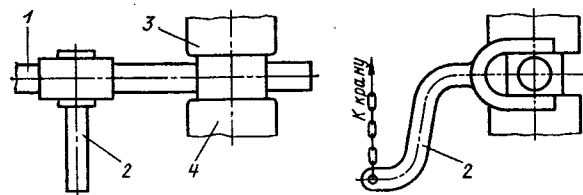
Схема скручивания: 1 — груз (противовес); 2 — изогнутая вилка; 3 — верхний боек; 4 — нижний боек
